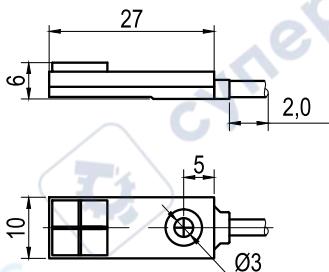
Габаритные и установочные размеры датчиков LKF10
